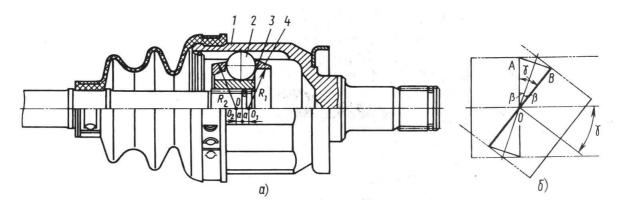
Шестишариковый универсальный шарнир: a — конструкция;  $\delta$  — схема; l — корпус; 2 — шарики; 3 — кулак; 4 — сепаратор
